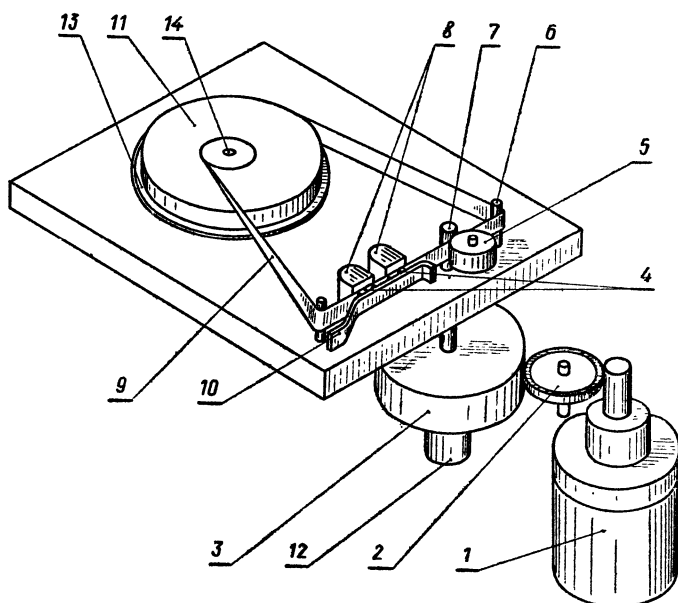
Упрощенная схема лентопротяжного механизма: 1 — электродвигатель; 2 — промежуточный ролик; 3 — маховик; 4 — фетровые прокладки; 5 — прижимный ролик; 6 — направляющий ролик; 7 — тонвал маховика; 8 — стереоголовки; 9 — петля ленты; 10 — рычаг; 11 — рулон бесконечной ленты; 12 — подпятник маховика; 13 — диск кассеты; 14 — ось кассеты
